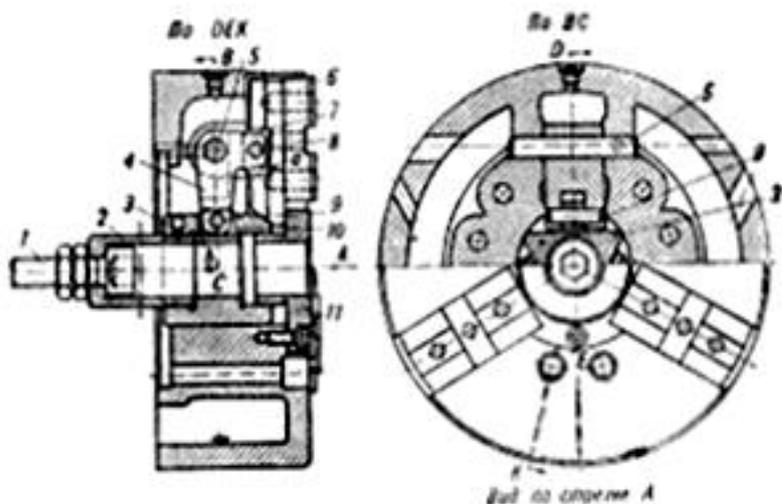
Общий вид трехкулачкового самоцентрирующего патрона с коленчато-рычажным механизмом
